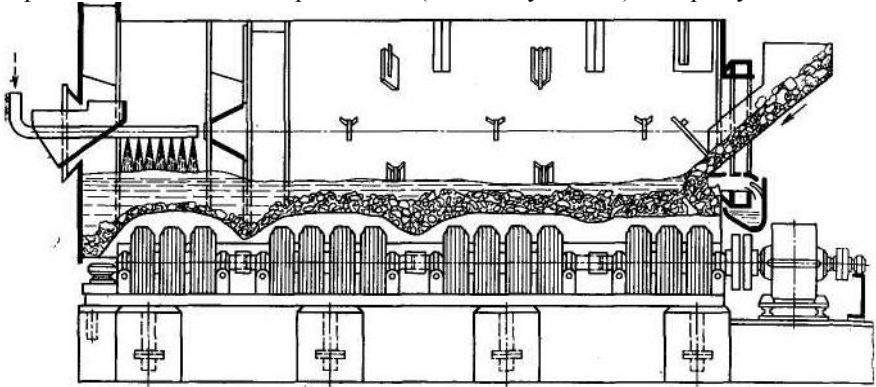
Принципова схема прямогочного барабана фірми Еш-Верке
